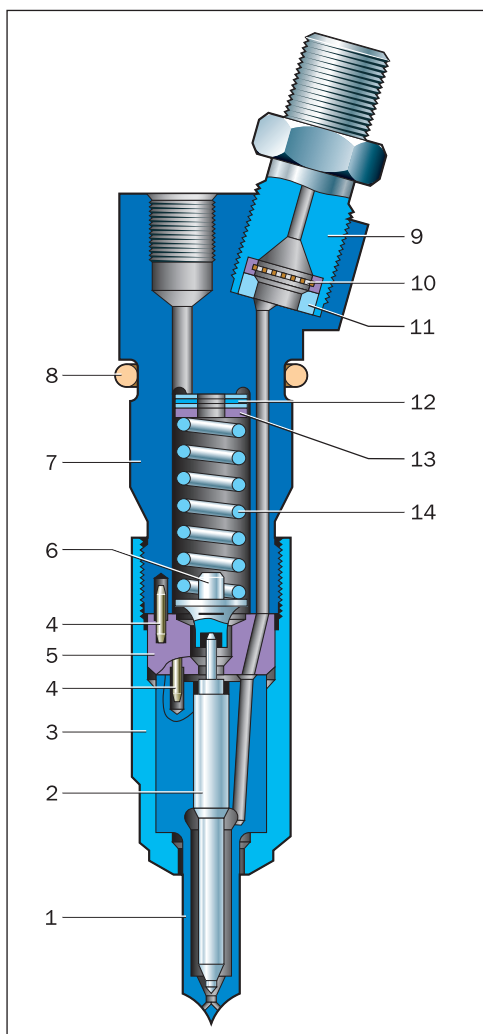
Конструкция многодырчатой форсунки: 1 — корпус распылителя; 2 — игла; 3 — гайка; 4 — установочные штифты; 5 — проставка; 6 — штанга; 7 — корпус форсунки; 8 — уплотнительное кольцо; 9 — штуцер; 10 — фильтр; 11 — уплотняющая втулка; 12 — регулировочные прокладки; 13 — упорная прокладка; 14 — пружина
